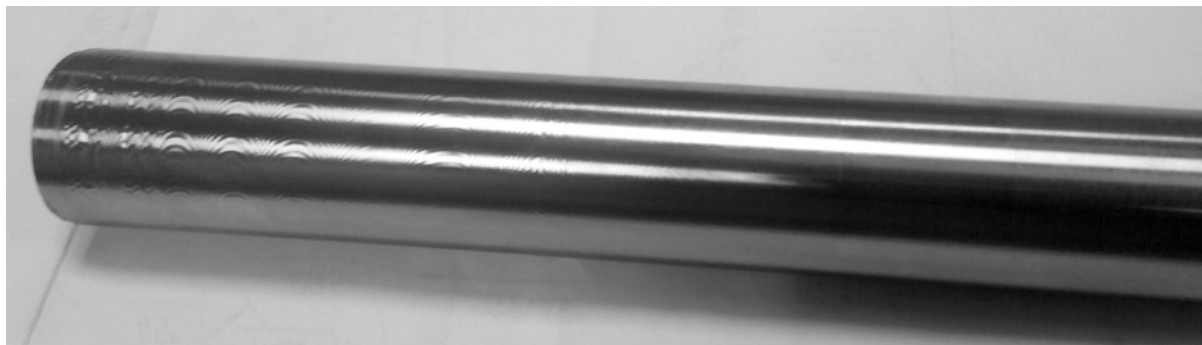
Результат обробки консольно закріпленої нежорсткої заготовки на режимах характерних для традиційної обробки
